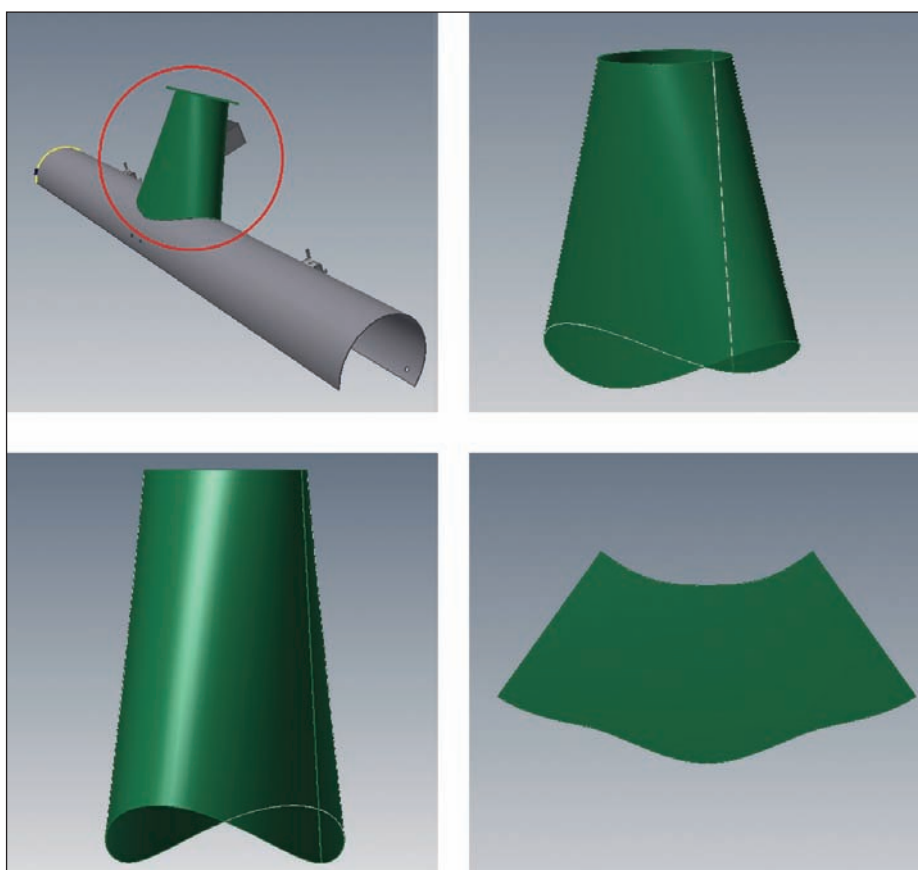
3D-модель и развертка детали загрузочного транспортера
